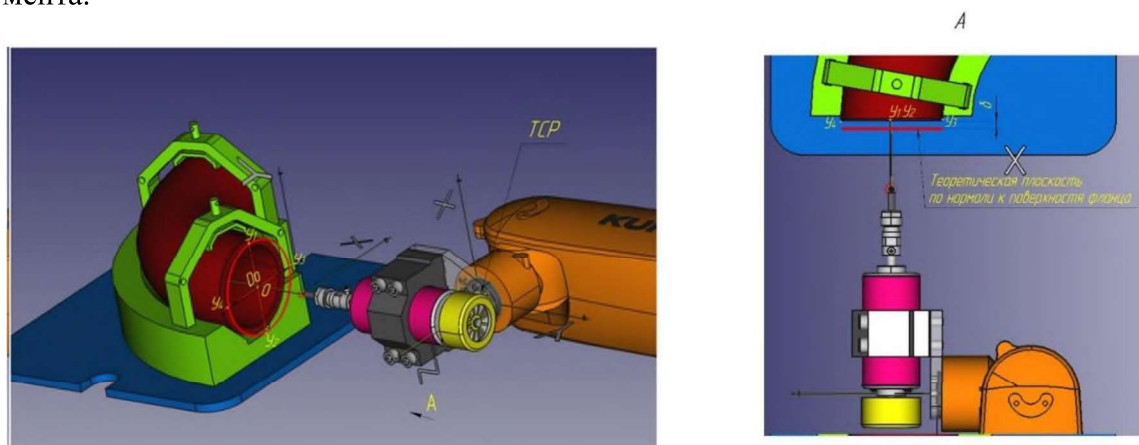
Схема калибровки инструмента относительно торца заготовки
